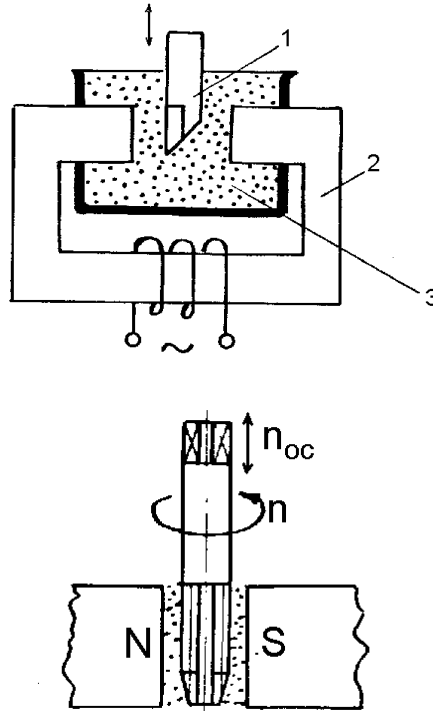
Схема заострения режущей кромки резца магнитно-абразивной обработкой.
